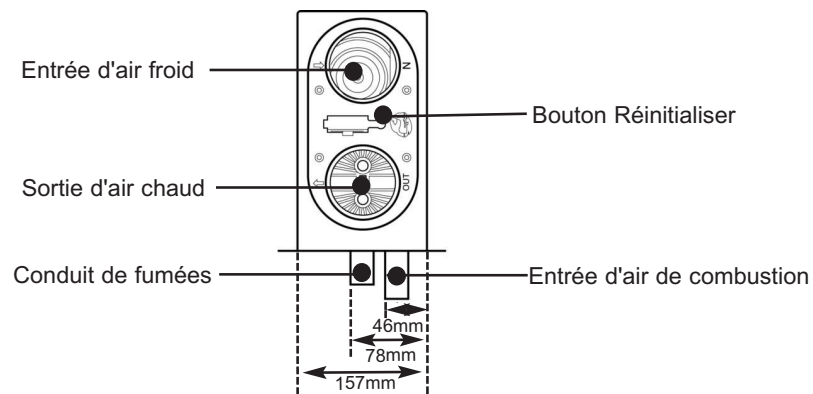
Installation interne - Vue frontale - SH2201 ou SC2201
